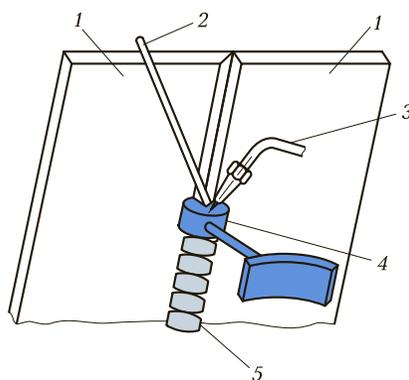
Схема сварки в кристаллизаторе:
